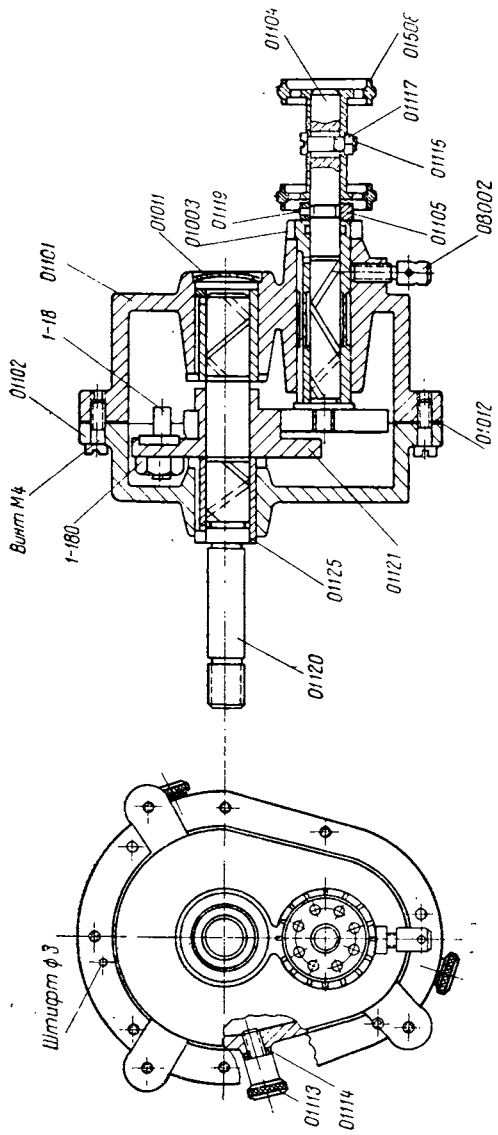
Мальтийский механизм передвигающего кинопроектора
